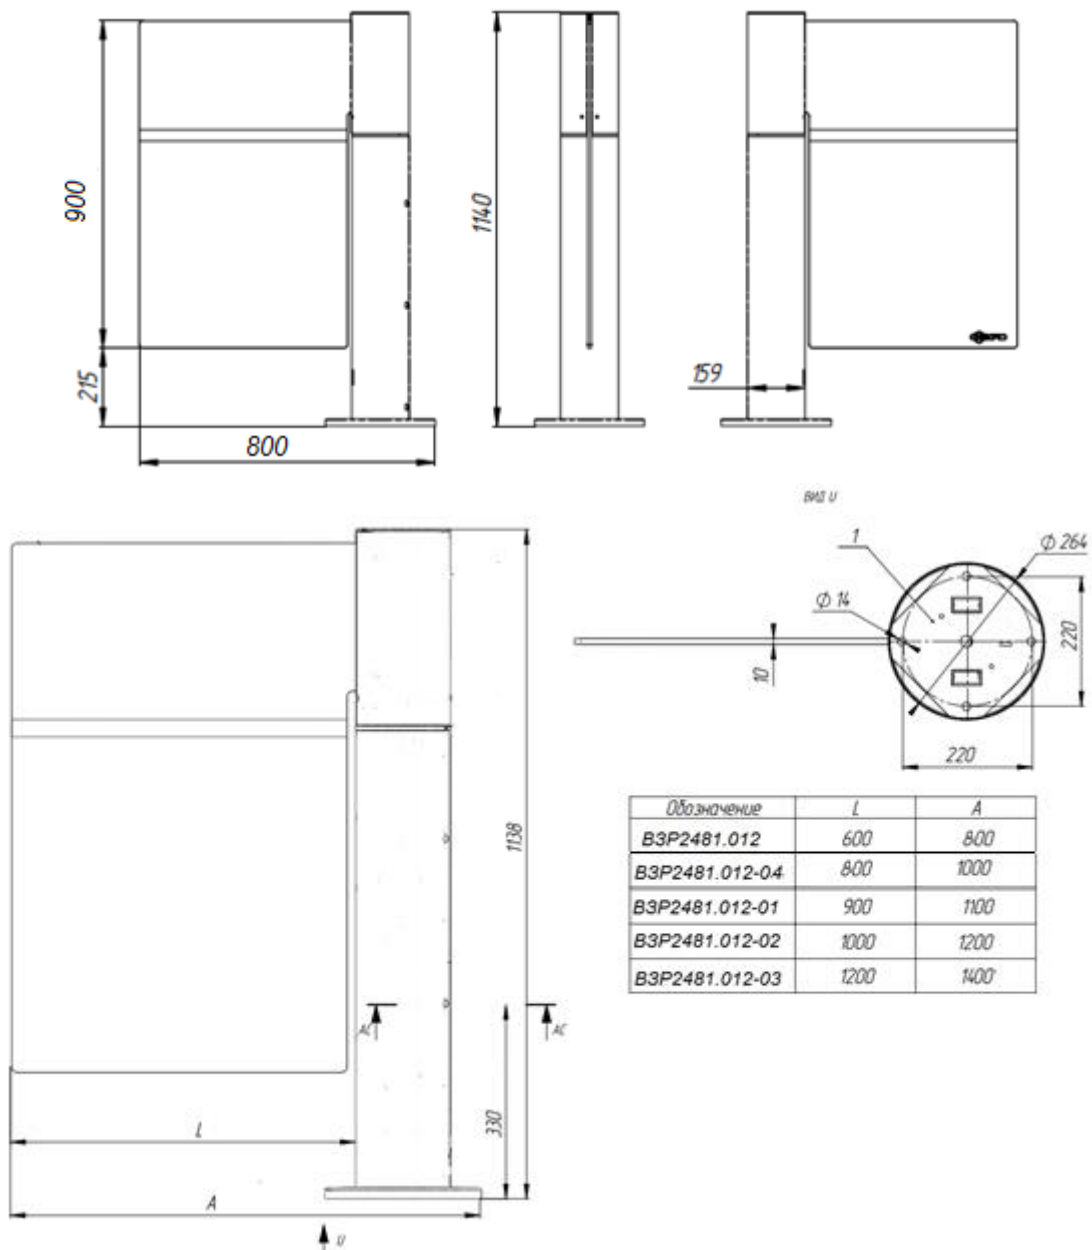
Габаритные размеры изделия для калитки со стеклом.
